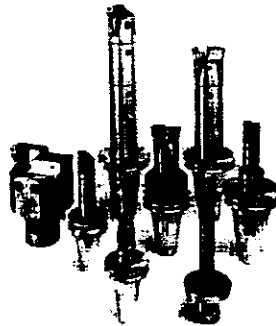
Herramientas para mandrinar con insertos de carburo.
